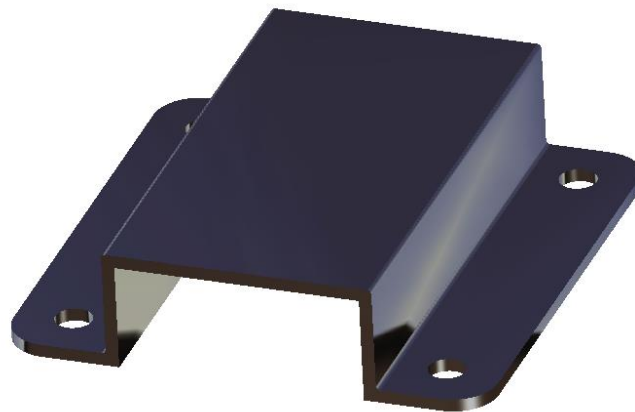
Abrazadera tipo omega para perfil 57x27mm
